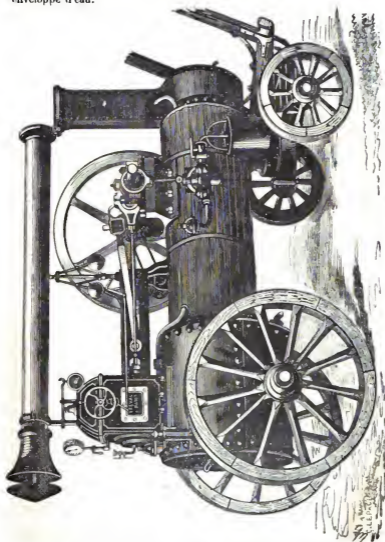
Machine à vapeur locomobile de M. Bréval.
